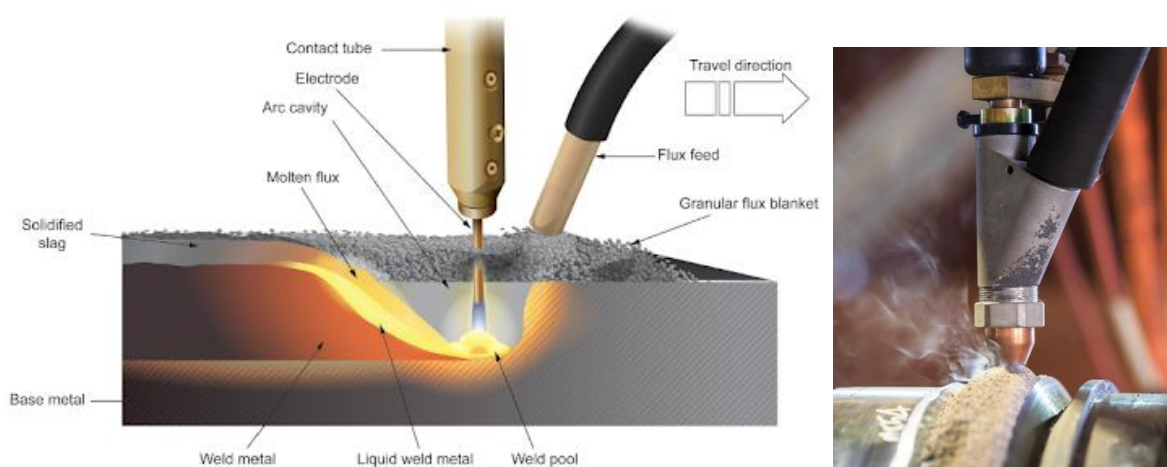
Схема автоматической сварки под флюсом
